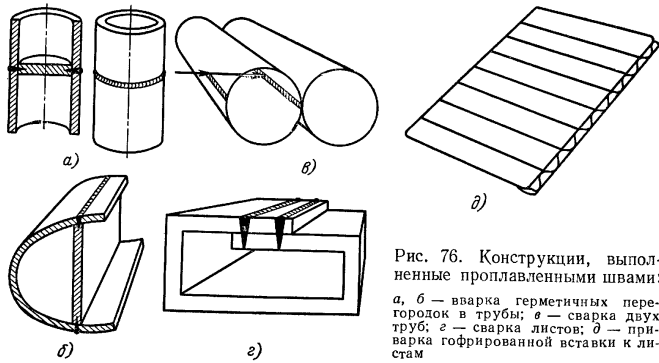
Конструкции, выполненные проплавленными швами: а, б — сварка герметичных перегородок в трубах; в — сварка двух труб; г — сварка листов; д — приварка гофрированной вставки к листам
